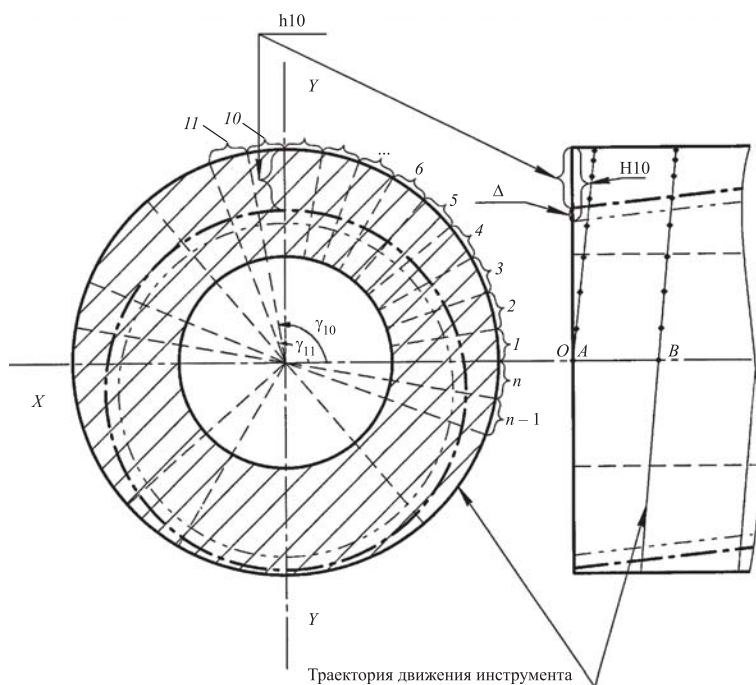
Схема разбивки линии траектории движения рабочего инструмента по обрабатываемой поверхности на элементарные участки
